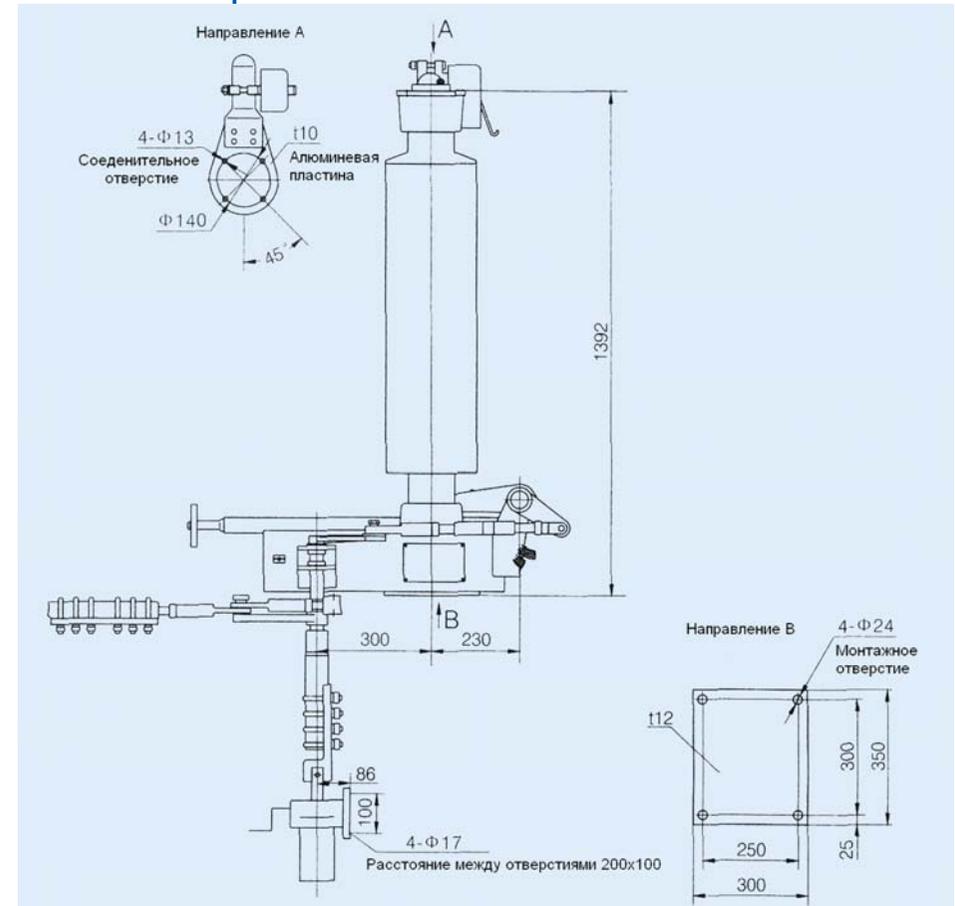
Внешний вид и размеры заземлителя JW□-126
